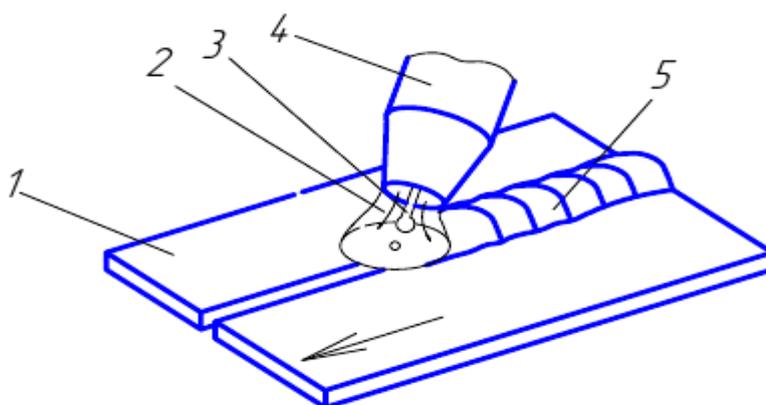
Схема сварки проволокой в защитных газах:
